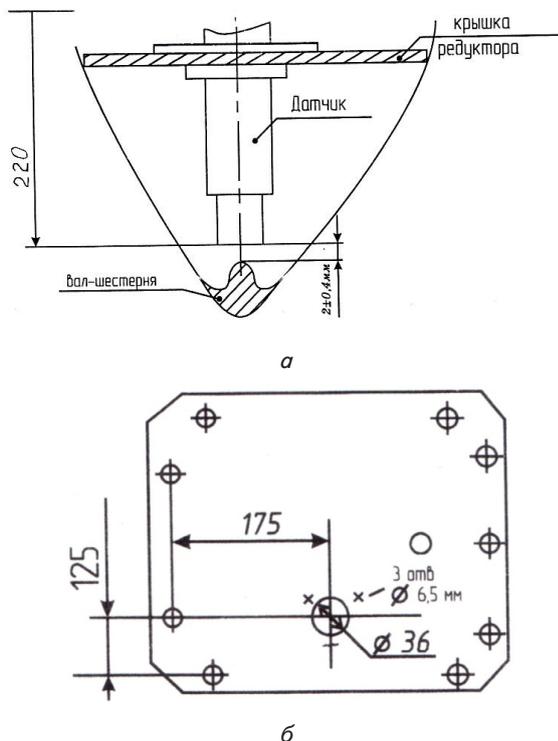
Схема установки датчика: а – размещение датчика относительно вал-шестерни; б – доработка крышки редуктора для крепления датчика
